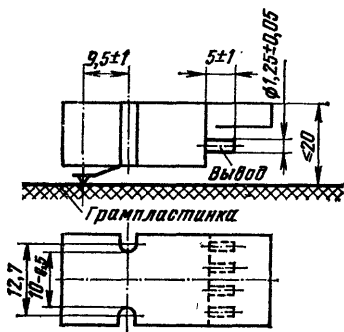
Установочные размеры головки звукоснимателя (рекомендации МЭК).
